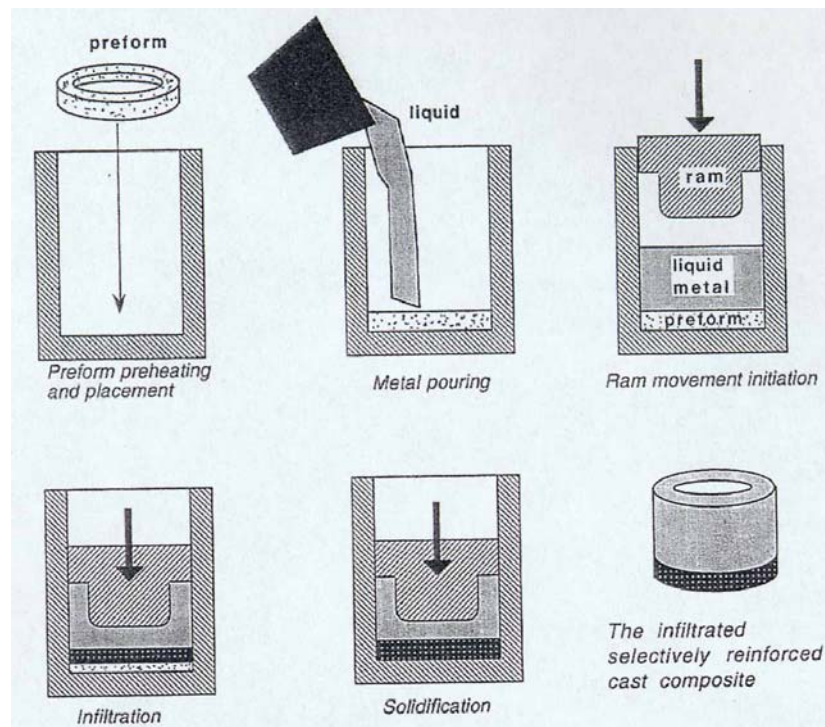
Schéma décrivant le procédé de « squeeze-casting »
